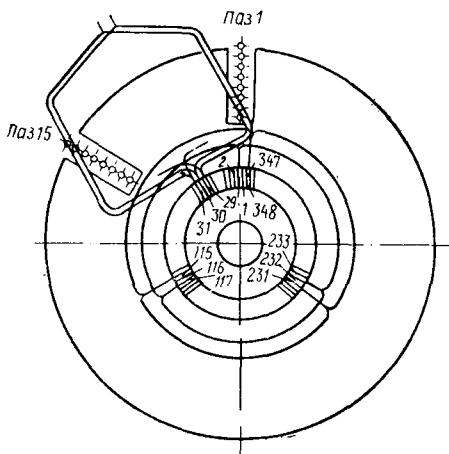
Схема соединения катушек якоря и уравнивателей с коллекторными пластинами тягового двигателя НБ-418К6 (вид со стороны коллектора)
